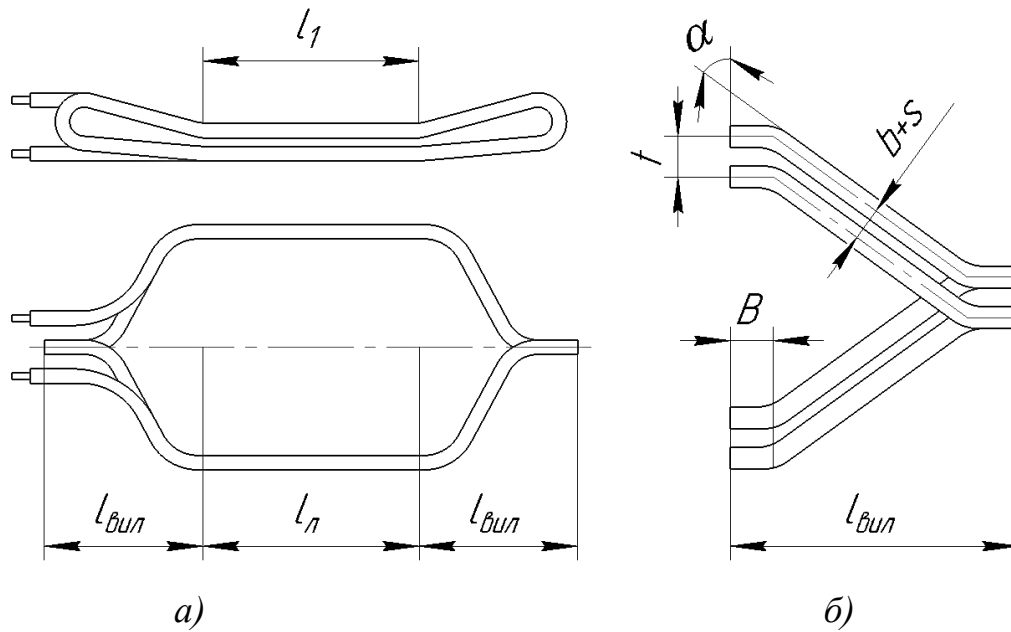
Котушка двошарової обмотки статора: а) загальний вигляд, б) розміри лобової частини котушки
